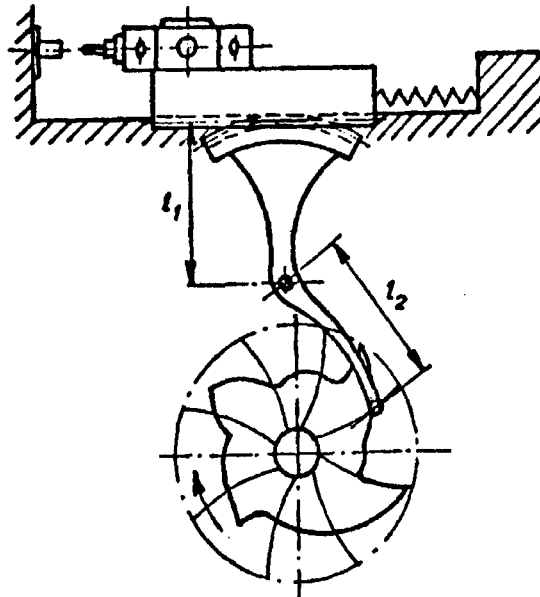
Rôzne druhy vačkových mechanizmov [6]
